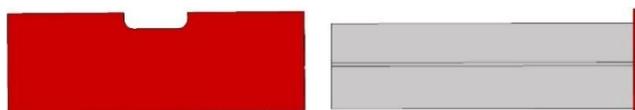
ALZADO Y PERFIL DEL CAJÓN CAJONERA
